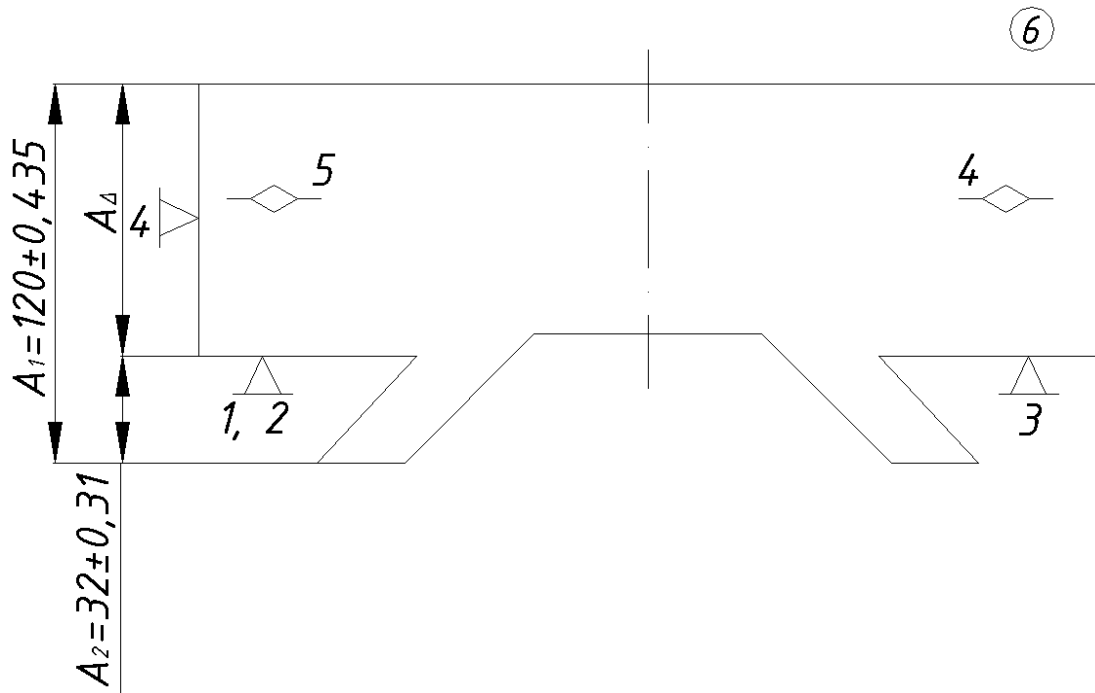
Схема базування заготовки при обробленні пов.б
